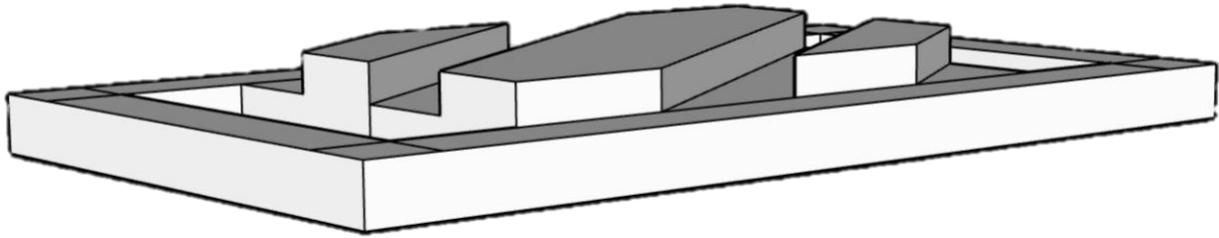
Perfil zapata metálica derecha. Elaboración propia.
